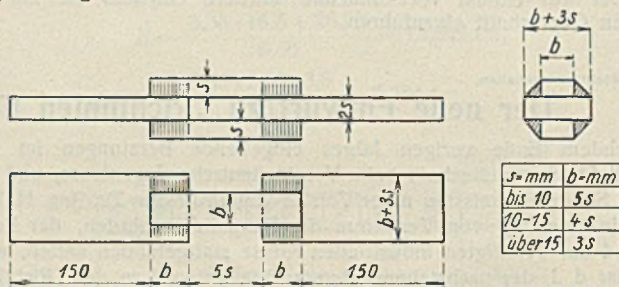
Probestück zur Schweißungsprüfung (Flankenkehlnähte).
